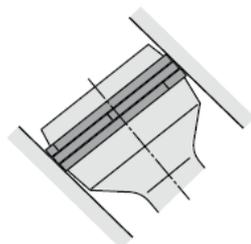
Поршень с многослойными поршневыми кольцами /35/
